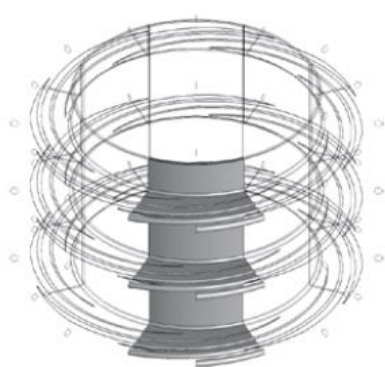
Схема конструкції п'ятишарової головки.
